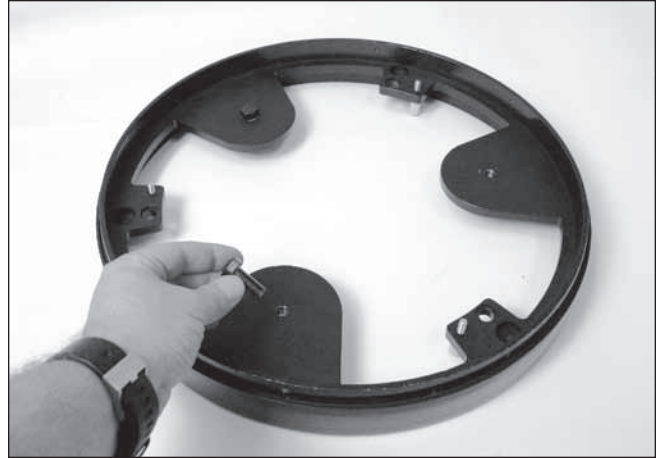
Führen Sie die drei Gegengewicht-Befestigungsschrauben in die Löcher des hinteren Endrings und ziehen Sie sie mit einem Schraubenschlüssel fest.
